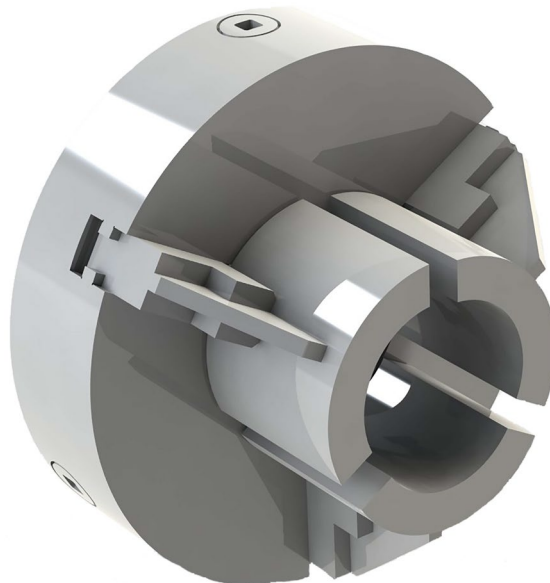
Конструкция патрона для зажима оболочечного корпуса
